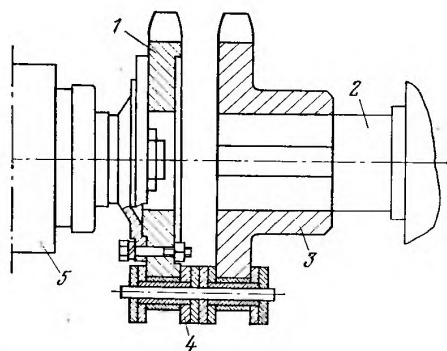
Муфта редуктора привода ротора экскаватора ЭТР231
